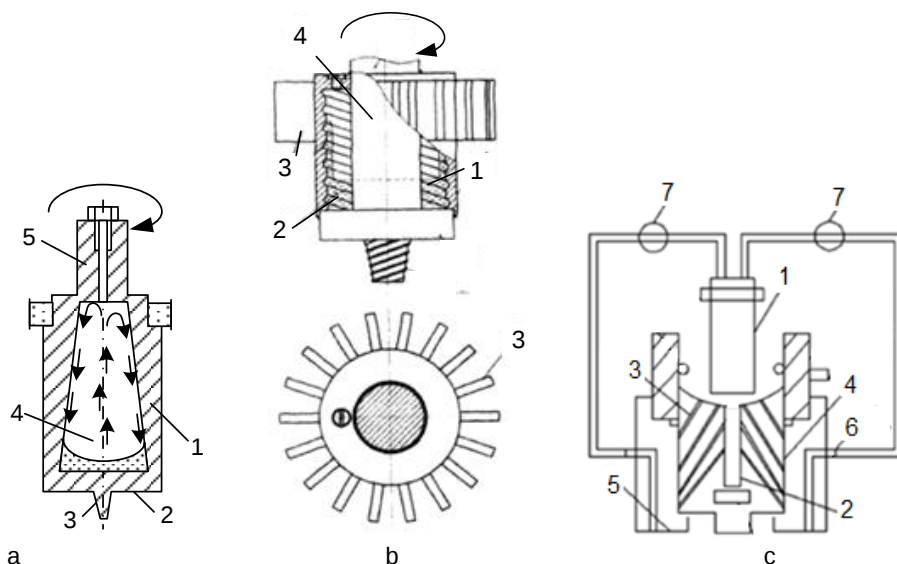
Системы охлаждения инструмента для сварки трением с перемешиванием
